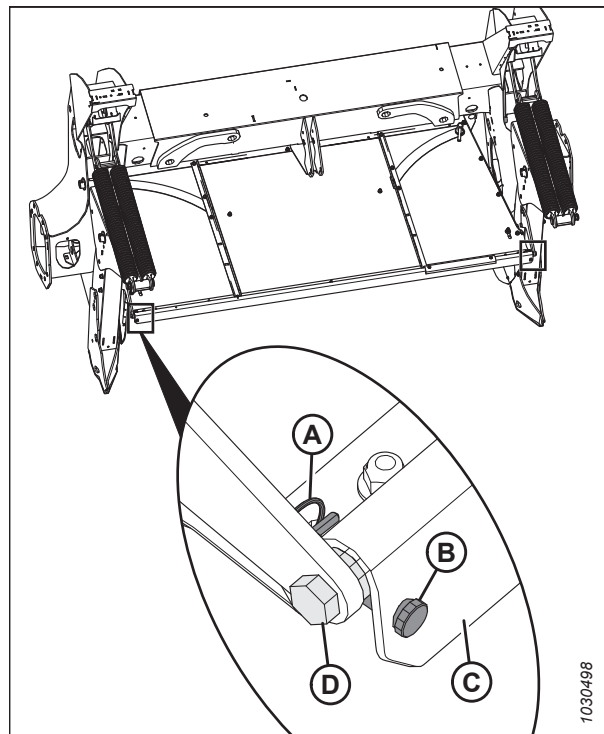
Резиновая стяжка для крепления формовочного щитка к лапе косилки
